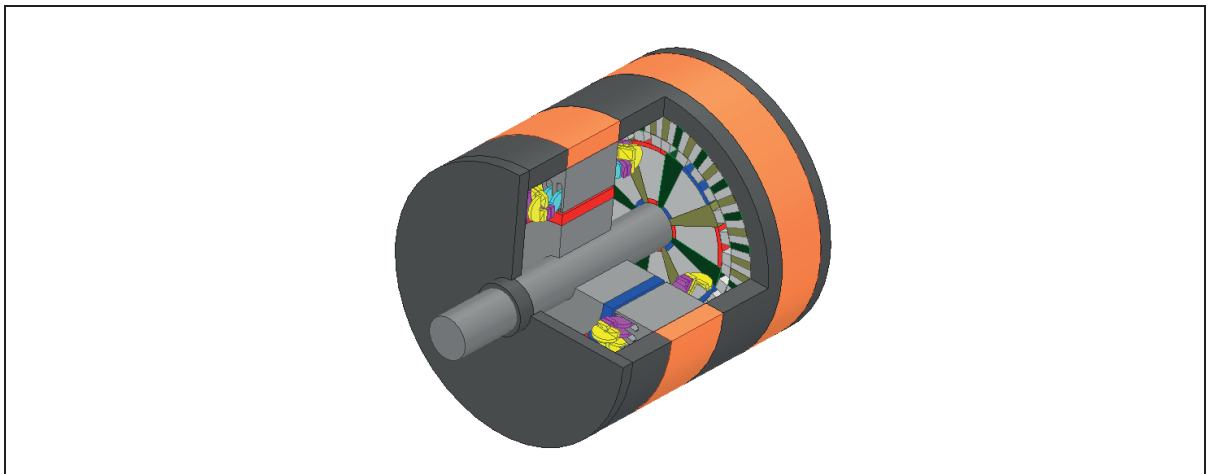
Vue en coupe de la machine à engrenage magnétique proposée
